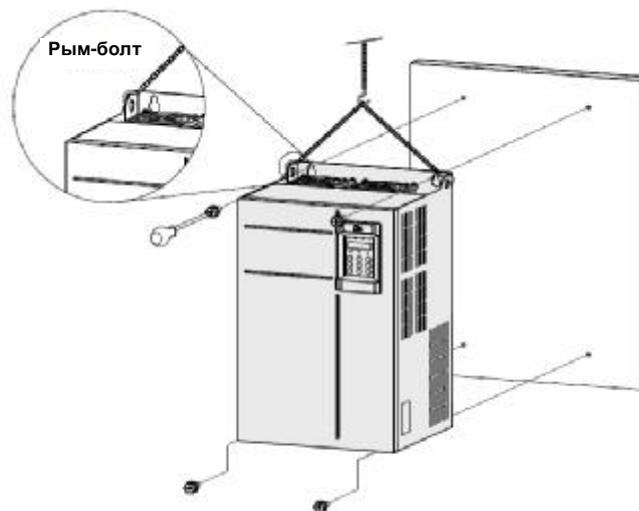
Настенный монтаж металлического корпуса MD500
